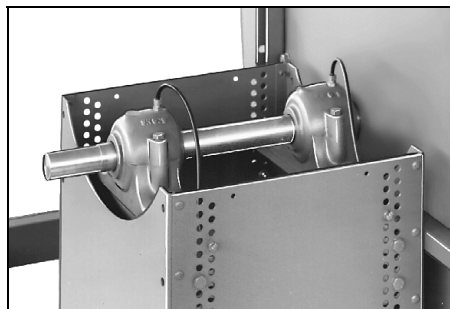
Pendelkugellager mit Steh-Gussgehäuse
